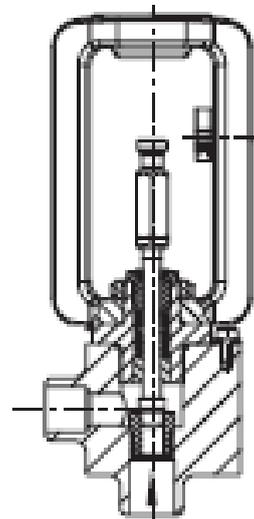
· Клапан высокого давления тип 3252 угловой с приварными концами
